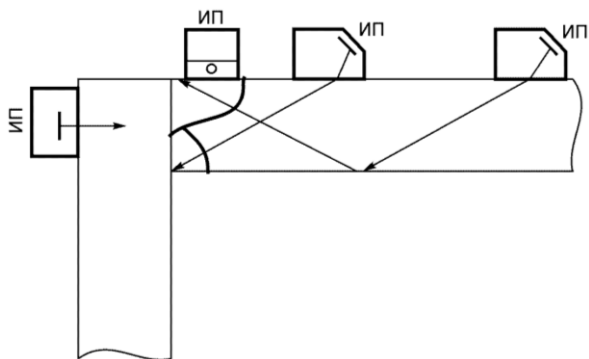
Схема прозвучивания углового сварного соединения совмещенными наклонными и прямым преобразователями
